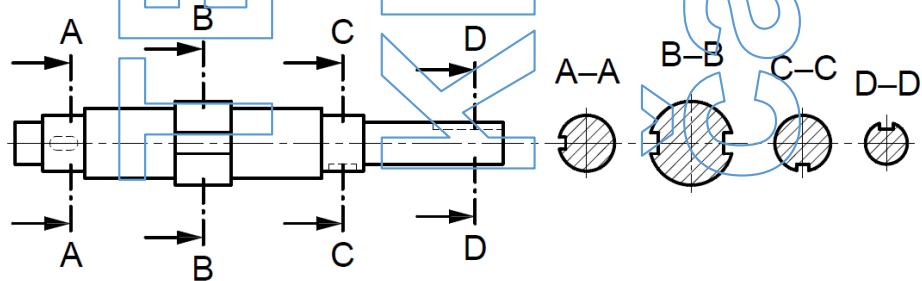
Príklad kreslenia vysunutého prierezu
